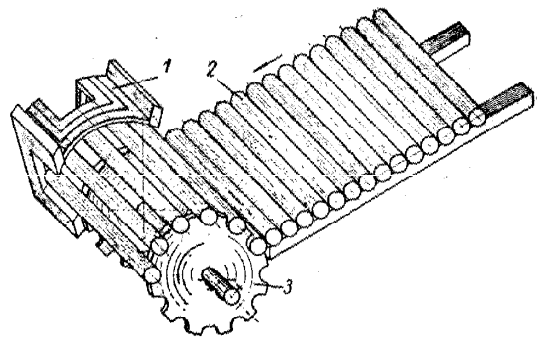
Схема нагревателя концов заготовок с щелевым индуктором:
